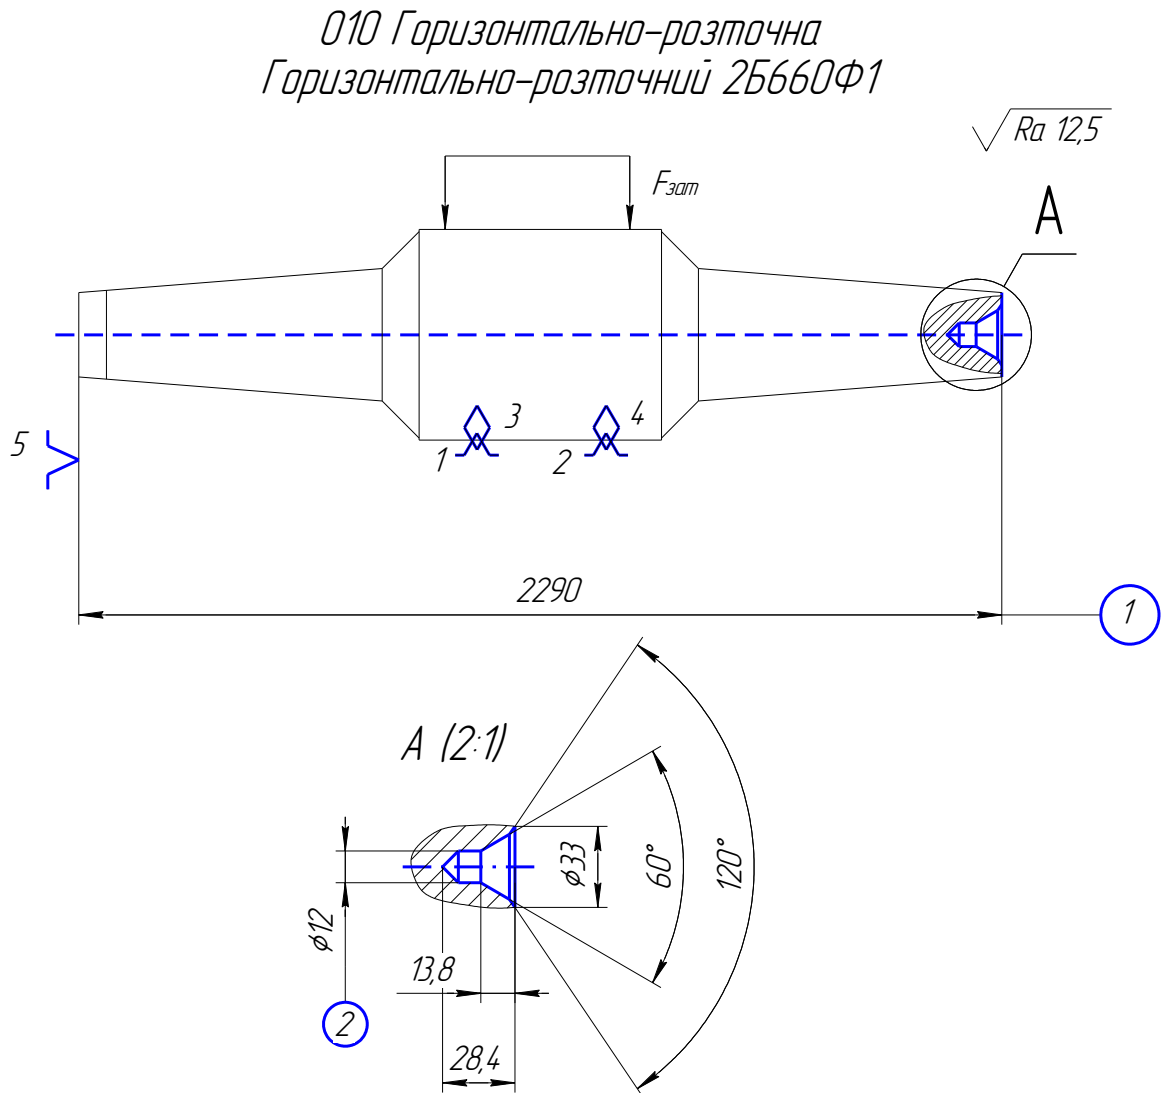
Ескіз механічної обробки деталі “Валок А”
